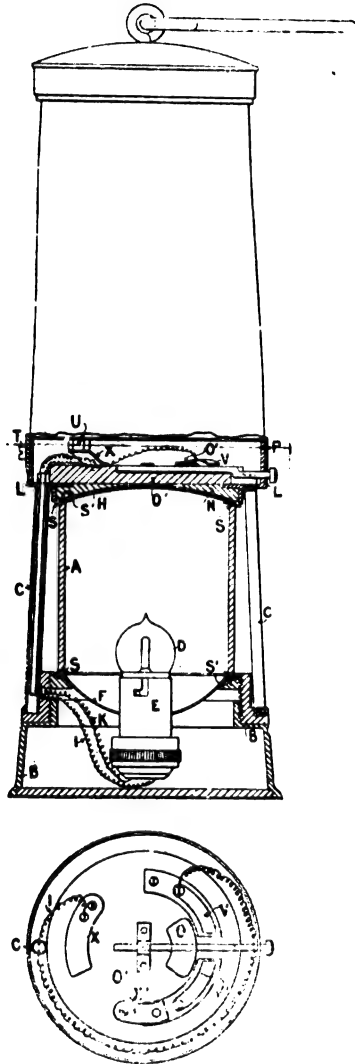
et 26. — Lampe de mineur Headland (1895).
